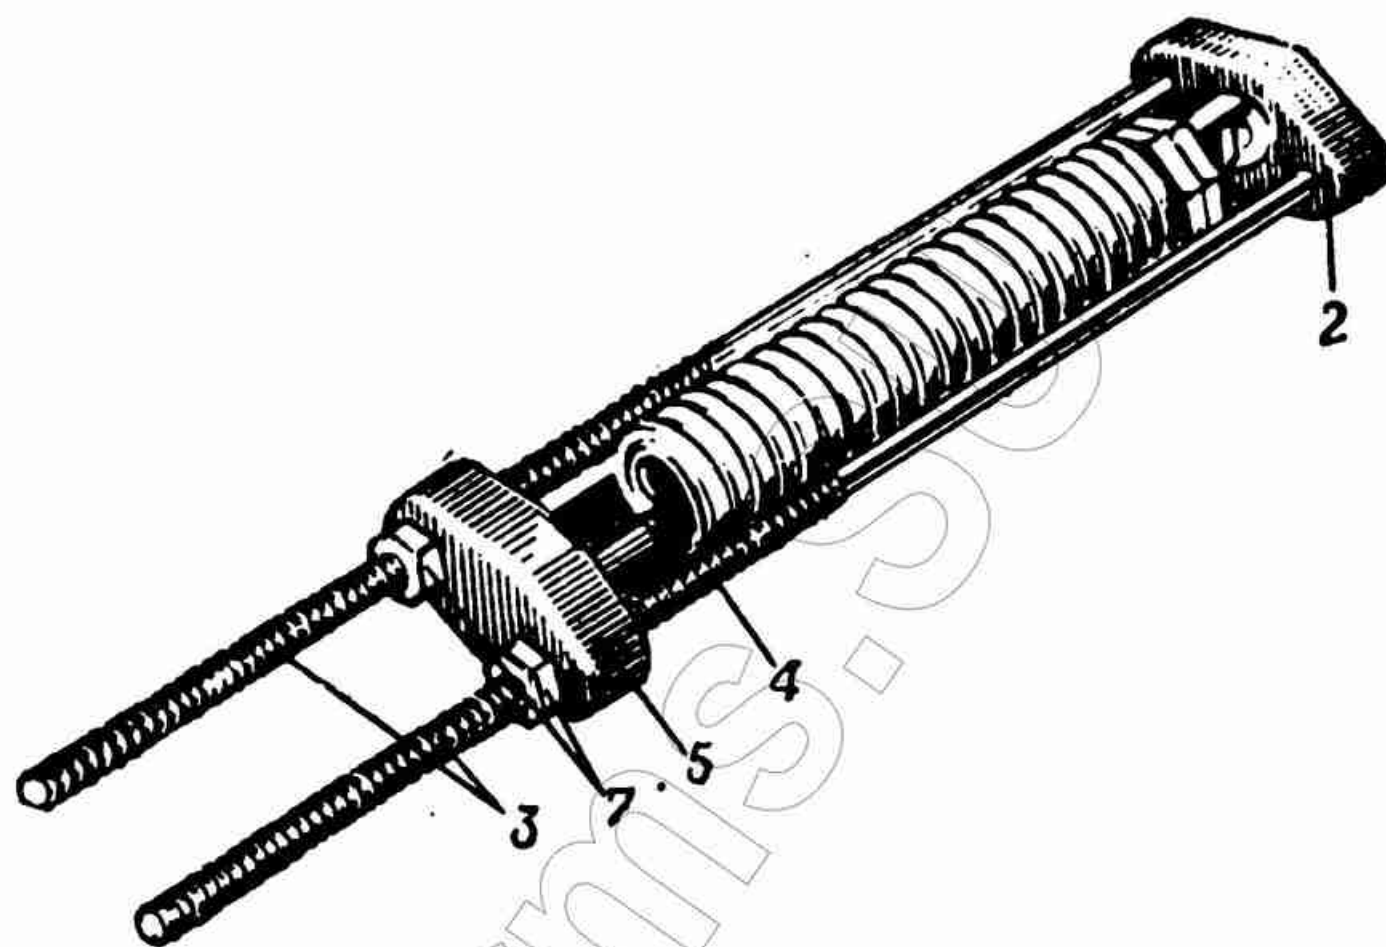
Прибор для разборки и сборки компенсирующего механизма:
